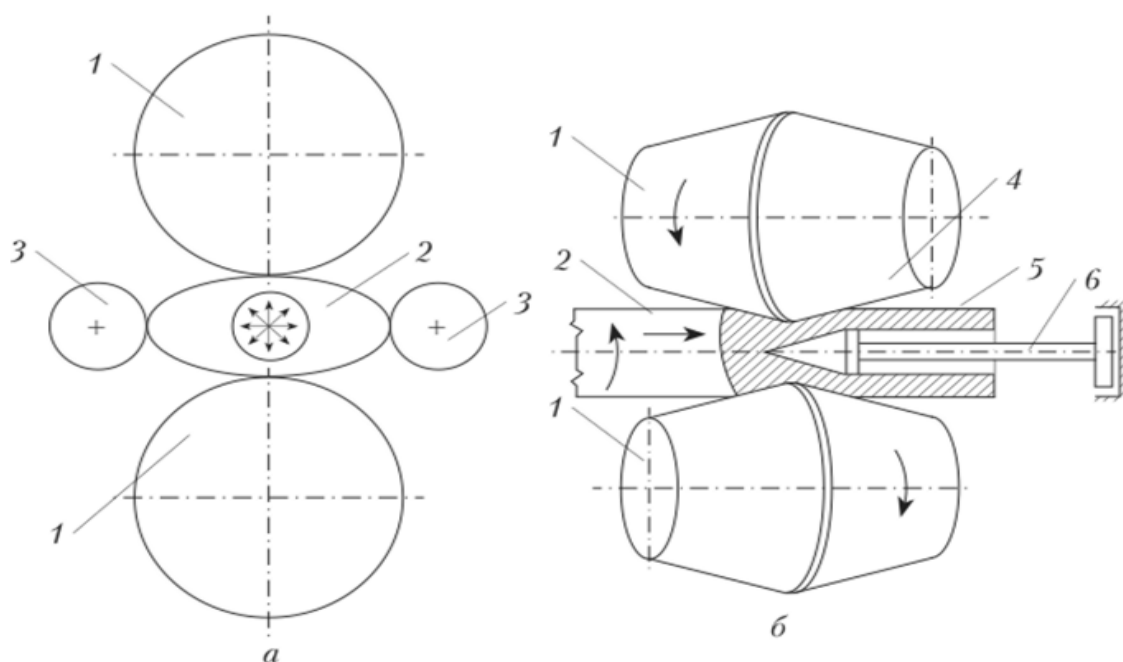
Поперечно-винтовая прокатка заготовки трубы [1]:
